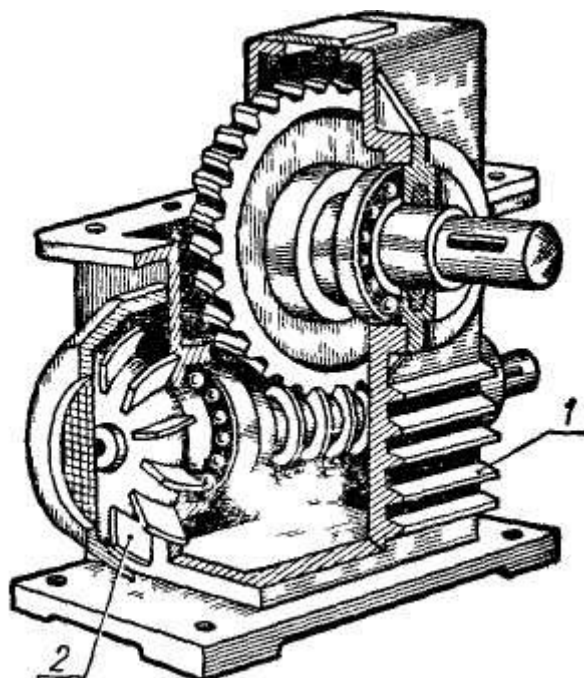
Охлаждение ребристого корпуса редуктора обдувом воздухом от вентилятора
